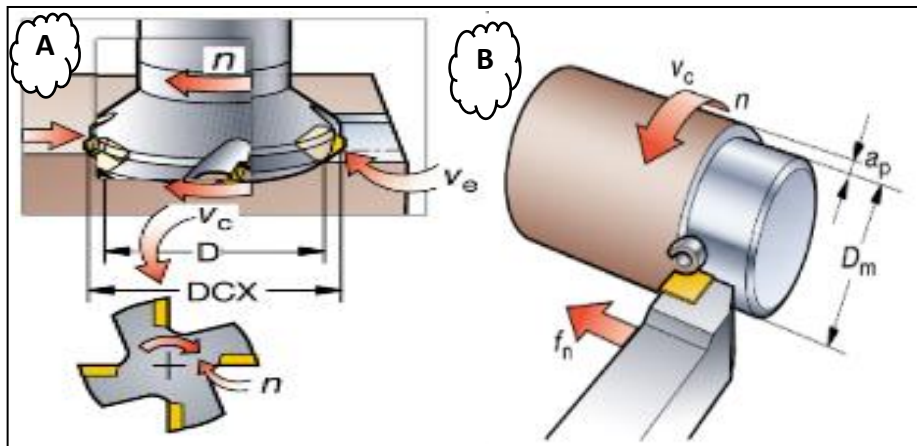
La vitesse de coupe. A) fraisage. B) tournage.
